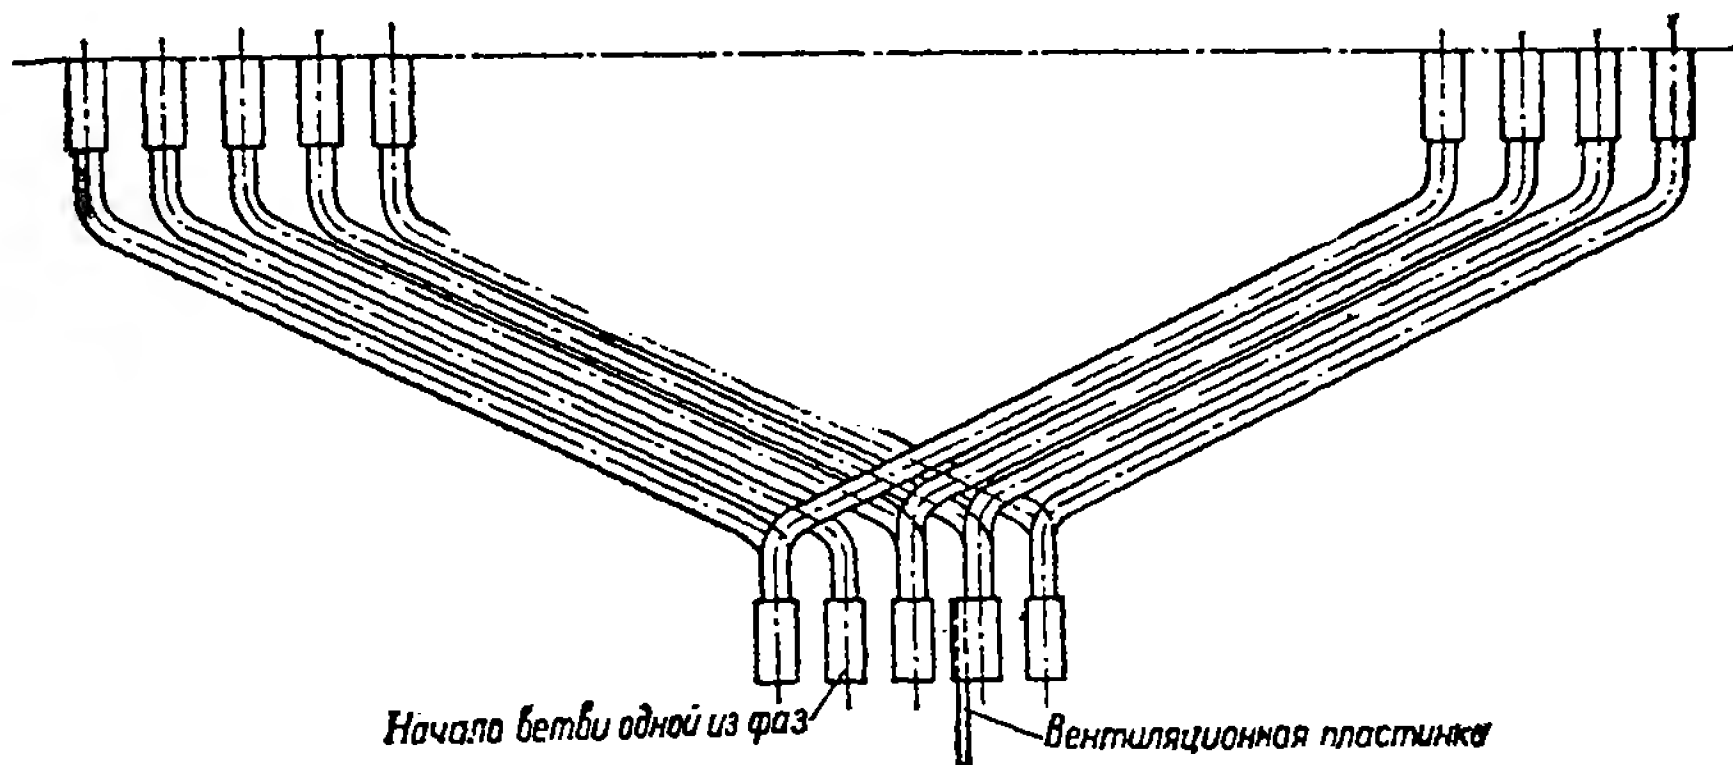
Лобовые соединения роторной обмотки асинхронного двигателя со стороны контактных колец.
